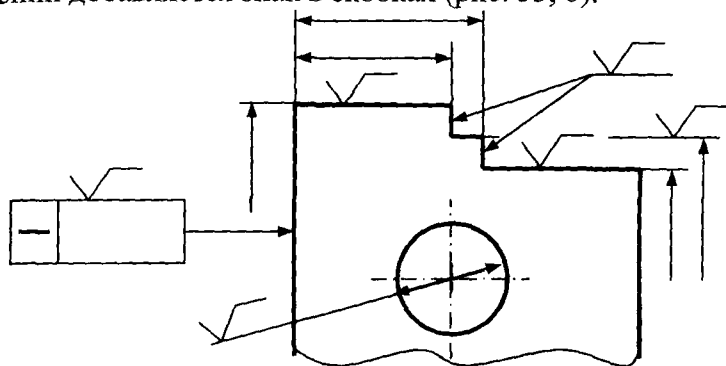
Примеры простановки знаков для обозначений требований к шероховатости
